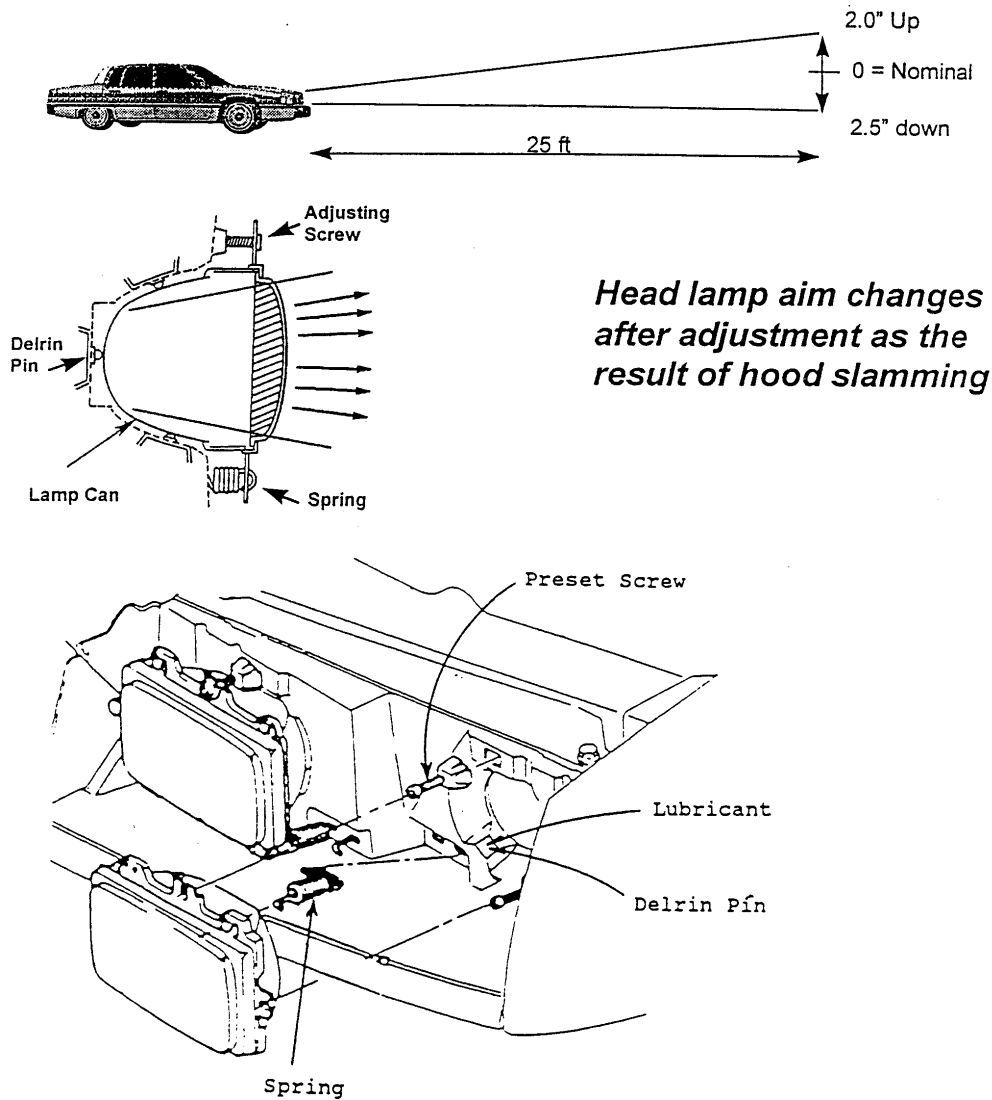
Cadillac 前大灯光束指向的质量问题的解决
